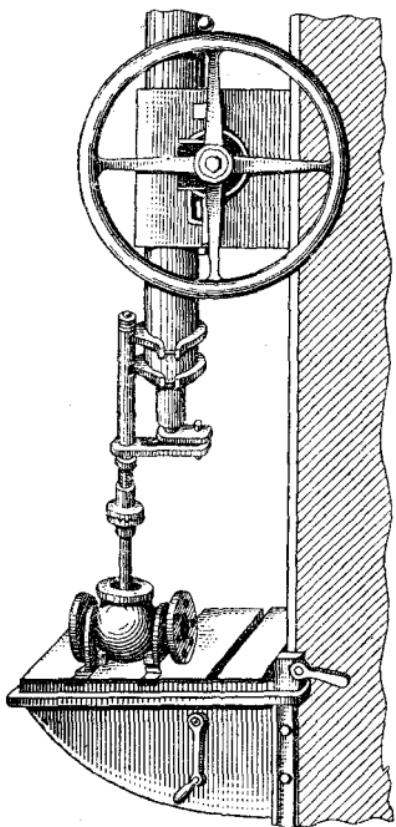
Приспособление для притирки арматуры на сверлильном станке
